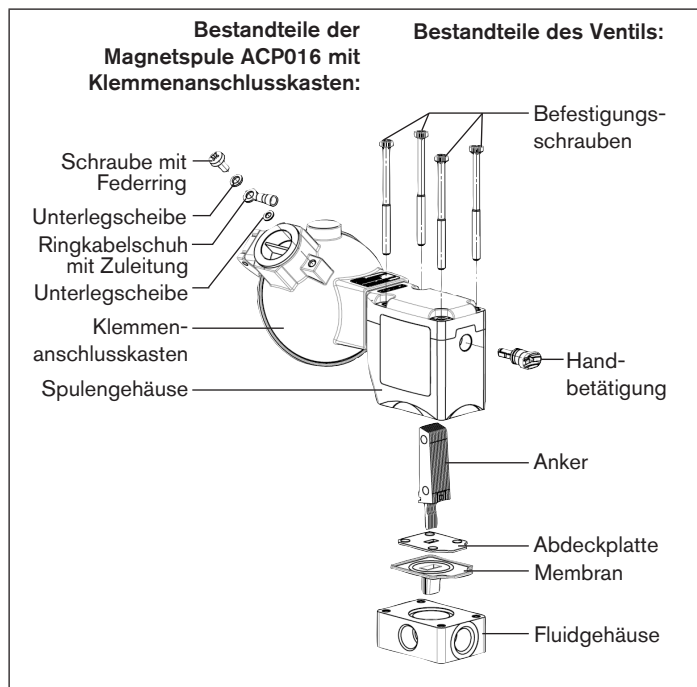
Ventil mit Magnetspule Typ ACP016 mit Klemmenanschlusskasten
